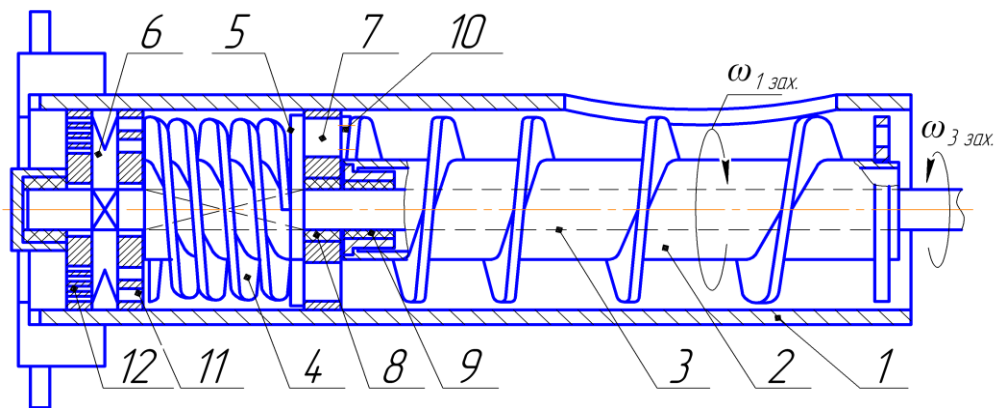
Устрій вовчка підвищеної продуктивності з двома коаксіальними шнеками зустрічного обертання: 1 – робочий циліндр; 2 – перший шнек; 3 – вал; 4 – другий дво- або тризахідний шнек; 5 – ніж попереднього подрібнення; 6 – ніж кінцевого подрібнення; 7 – решітка попереднього подрібнення; 8, 9 – підшипники ковзання; 10 – лезо; 11 – приймальна решітка; 12 – вихідна решітка
